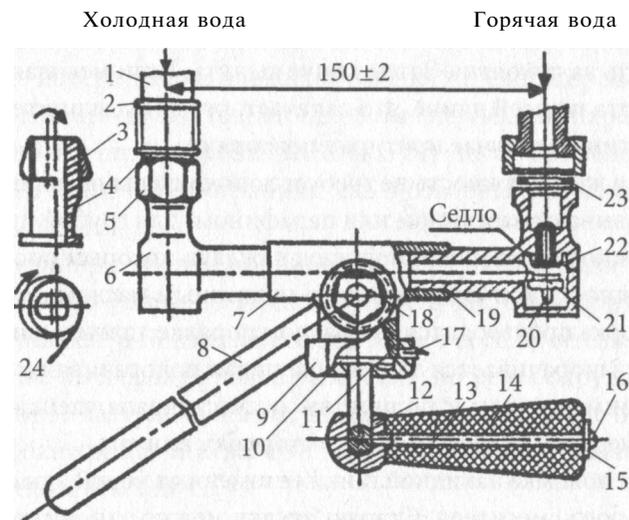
Смеситель с пробковым переключателем «ванна — душ»: 1 — подводная труба; 2 — муфта; 3 — уплотнение втулки; 4 — эксцентрическая втулка; 5 — накидная гайка; 6 — боковина; 7 — корпус; 8 — излив; 9 — накидная гайка; 10 — шайба латунная; 11 — ограничитель; 12 — остов; 13 — ось; 14 — рукоятка; 15 — шайба; 16 — специальный винт; 17 — стопорный винт; 18 — конус (пробка); 19 — уплотнение; 20 — клапан; 21 — прокладка головки крана; 22 — втулка ремонтная; 23 — прокладка накидной гайки; 24 — направление намотки Уплотнения
